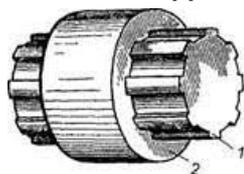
Зубчатое (шлицевое) соединение: 1 — вал; 2 — ступица колеса
